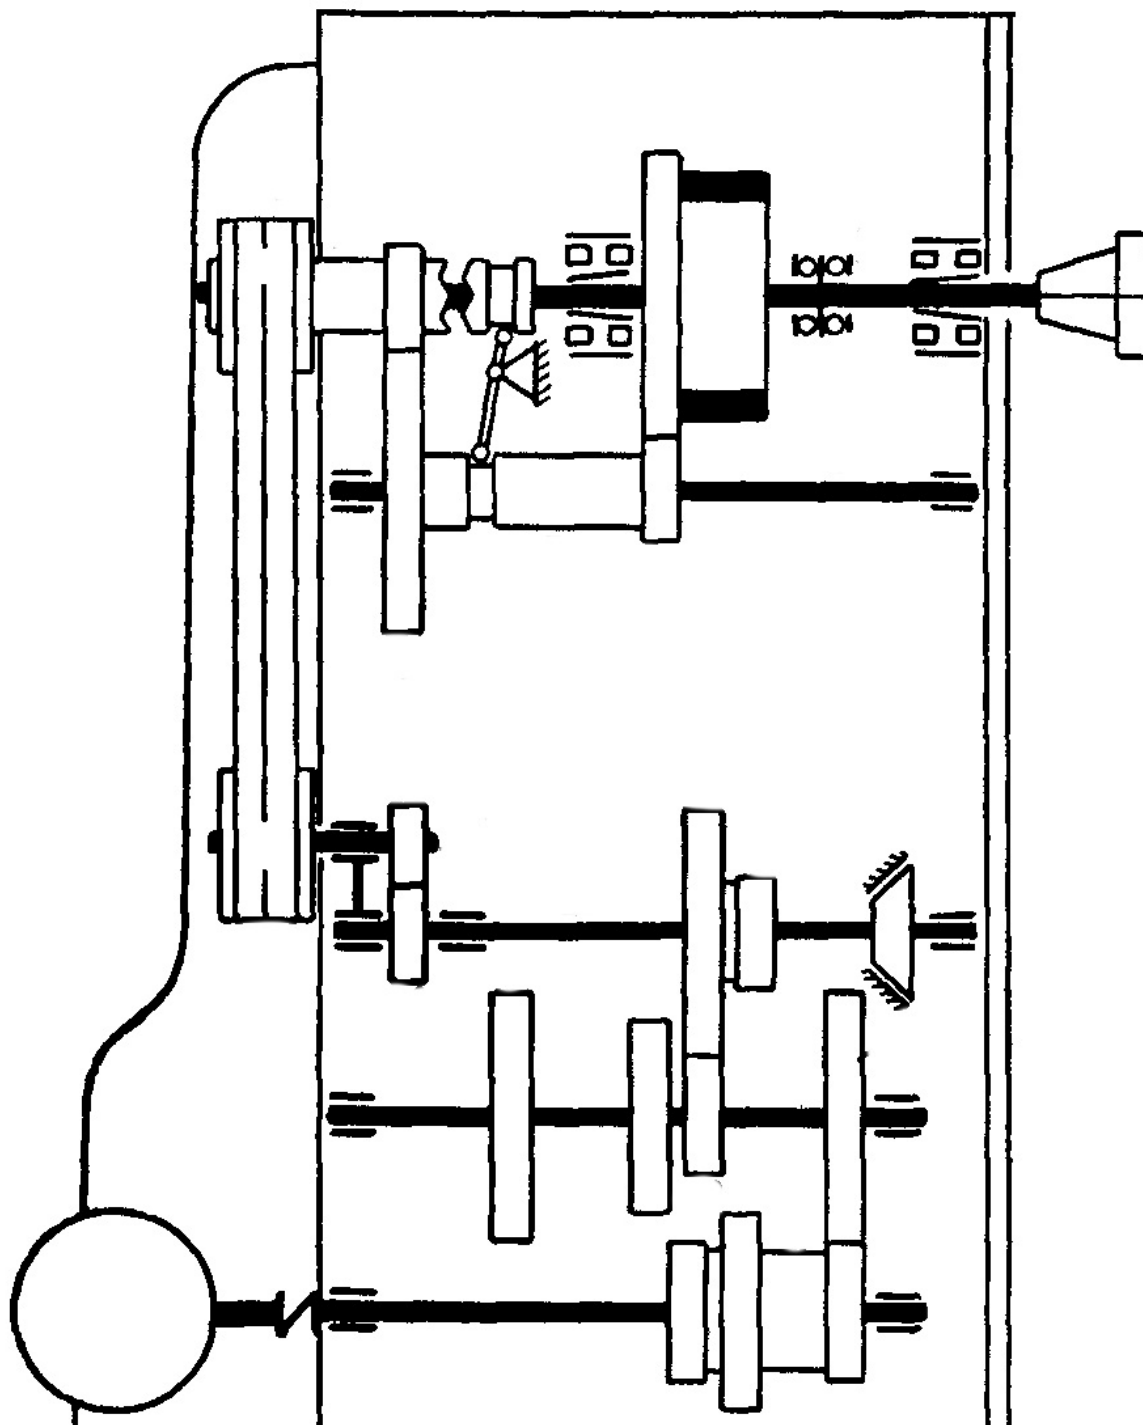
Німа кінематична схеми коробки швидкостей токарного верстата
